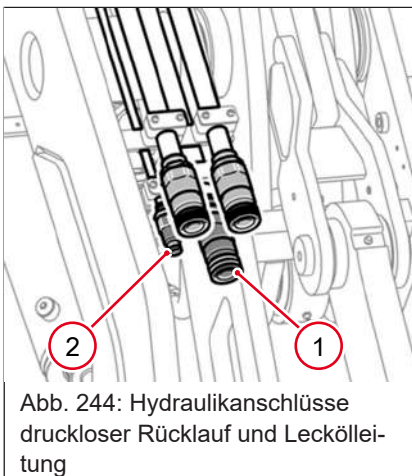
Hydraulikanschlüsse druckloser Rücklauf und Leckölleitung
